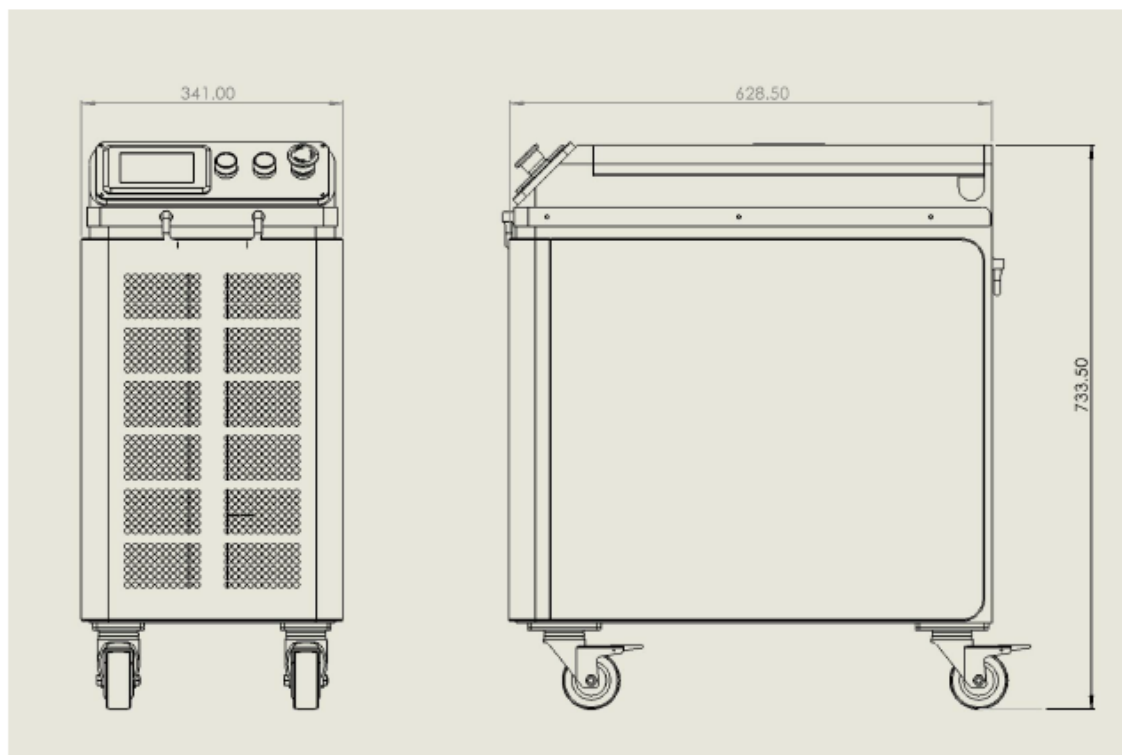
Dimensões gerais da máquina de limpeza a laser SLC-300
